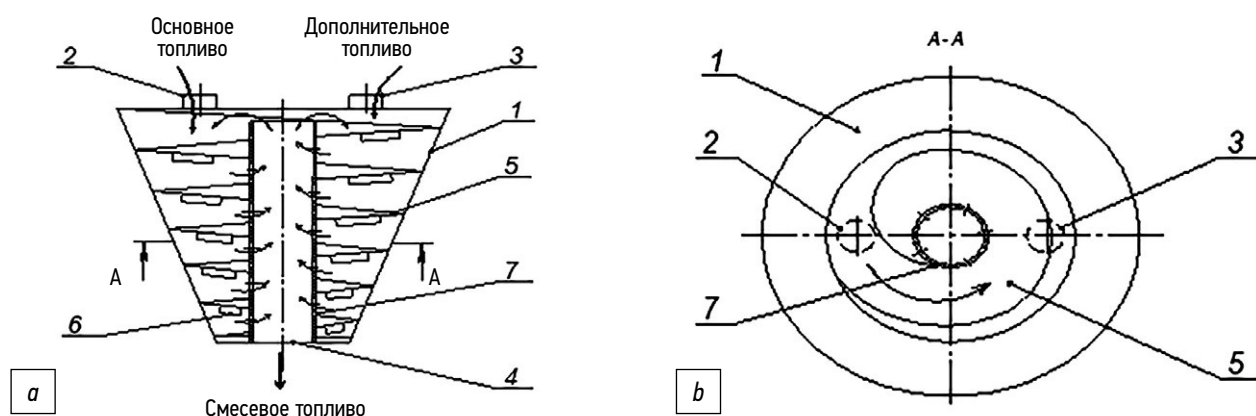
Схема смесительной установки: *a* — вид спереди; *b* — разрез; 1 — корпус; 2, 3 — окна подачи основного (дизельного) и дополнительного топлива; 4 — окно для выхода МСТ; 5 — шнек; 6 — лопасти; 7 — перфорированный цилиндр.
